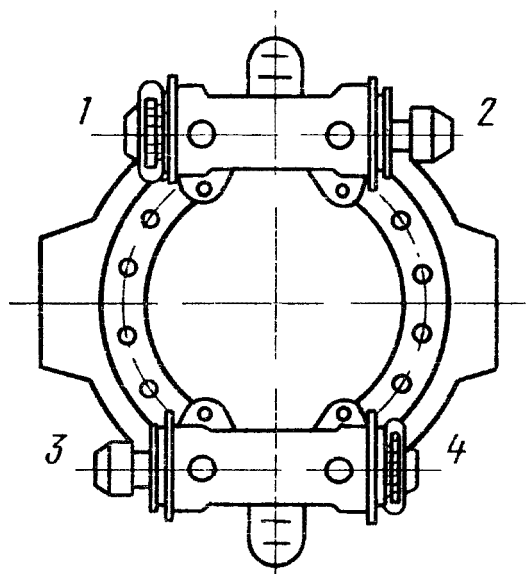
Схема расположения регулировочных винтов и втулок тормозного механизма переднего колеса
